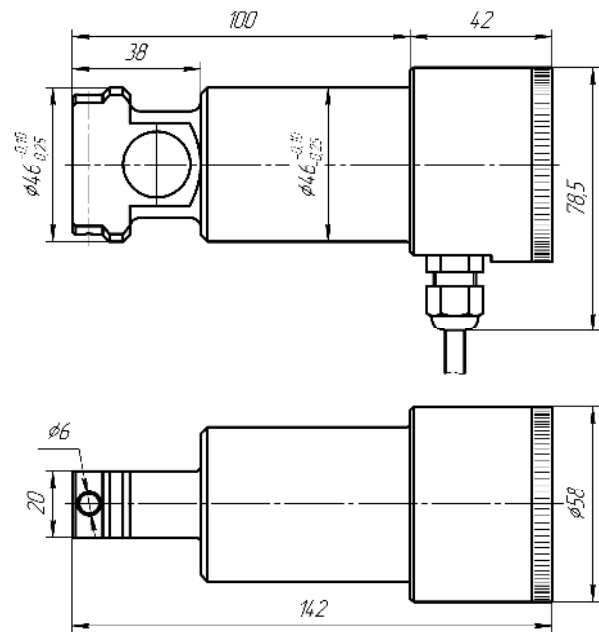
Корпус тип 0. Габаритные и присоединительные размеры.
